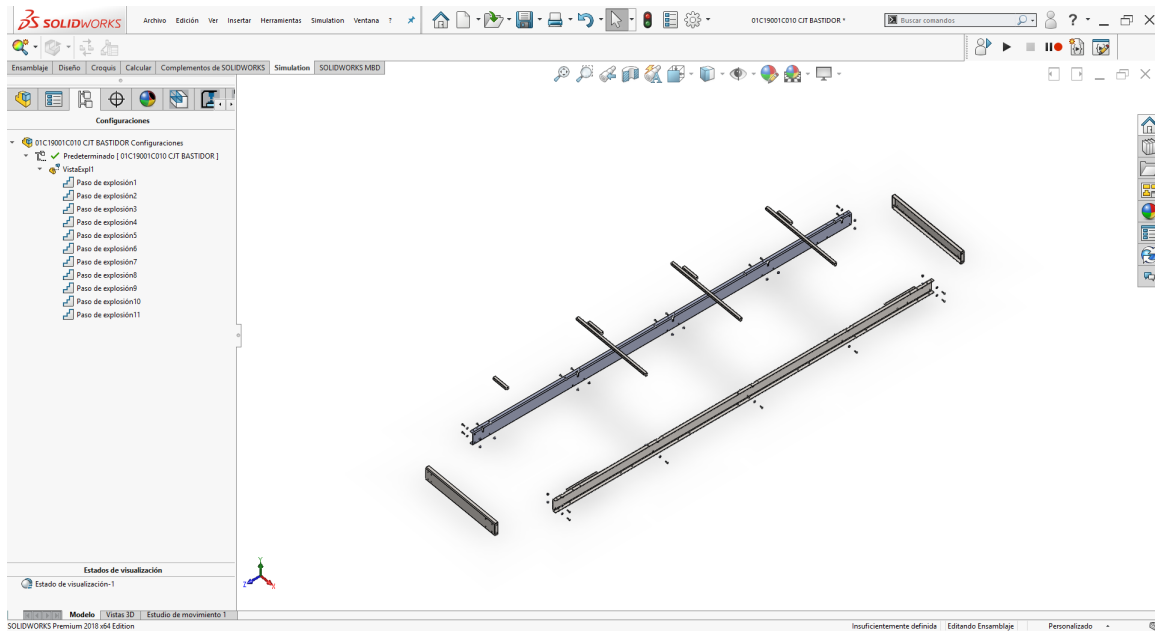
Esquema general y posiciones del bastidor. vista explosionada
